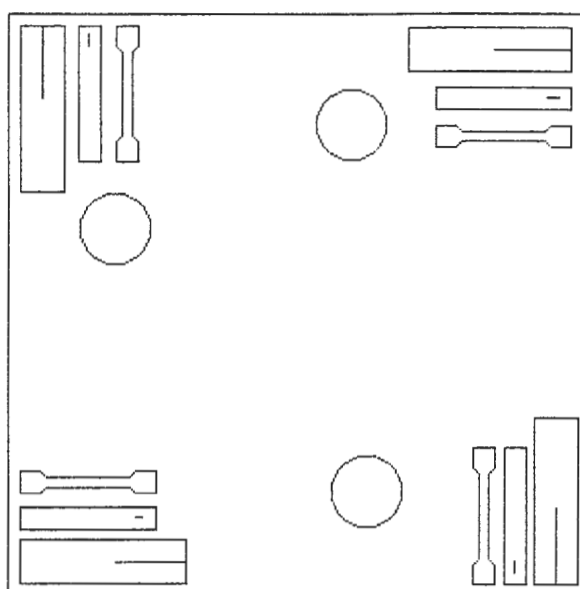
Emplacement des éprouvettes sur l'échantillon
